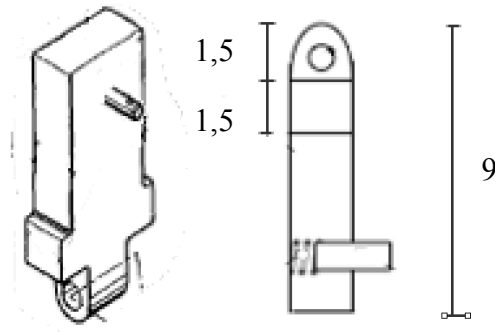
Dimensiones de las barras con cilindro sobresaliente que se introducen en la barra hueca con ranura.
